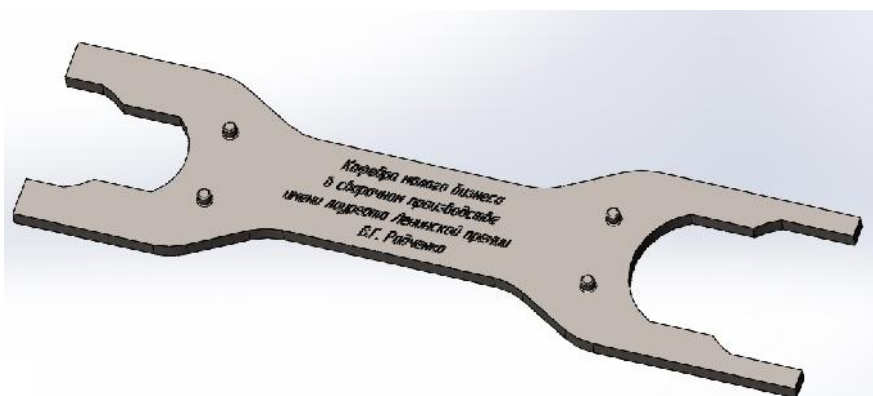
Специализированный ключ для сборки сверхзвукового устройства для наплавки (с гравировкой)
